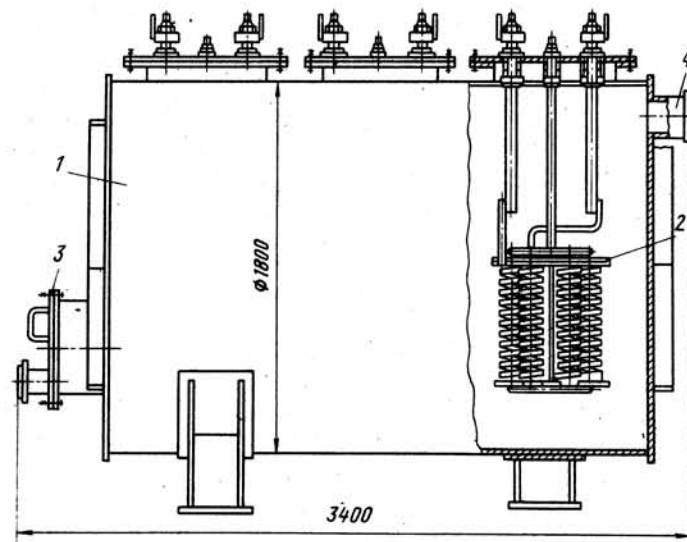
Схема куба-испарителя: 1 — корпус; 2 — погружной электронагреватель из ленточного нихрома; 3 — люк; 4 — патрубок для пара
